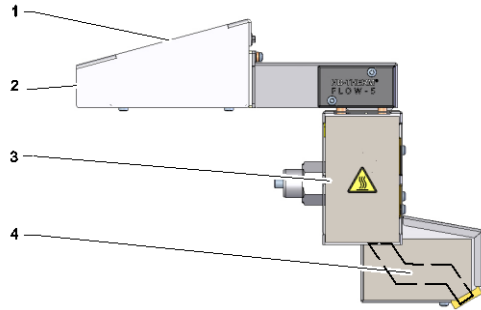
Privire de ansamblu asupra modului de construcție: Construcția aparatului
